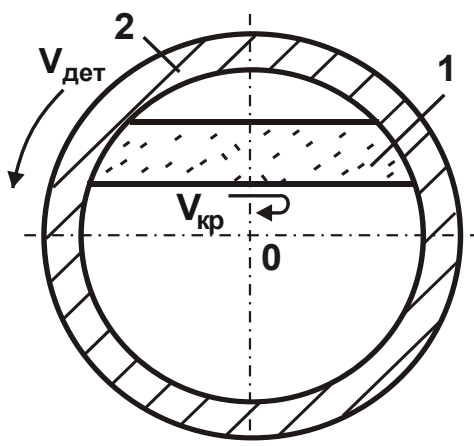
Схема шлифования с перпендикулярным расположением осей вращения круга и детали: 1 – круг; 2 – обрабатываемая деталь
